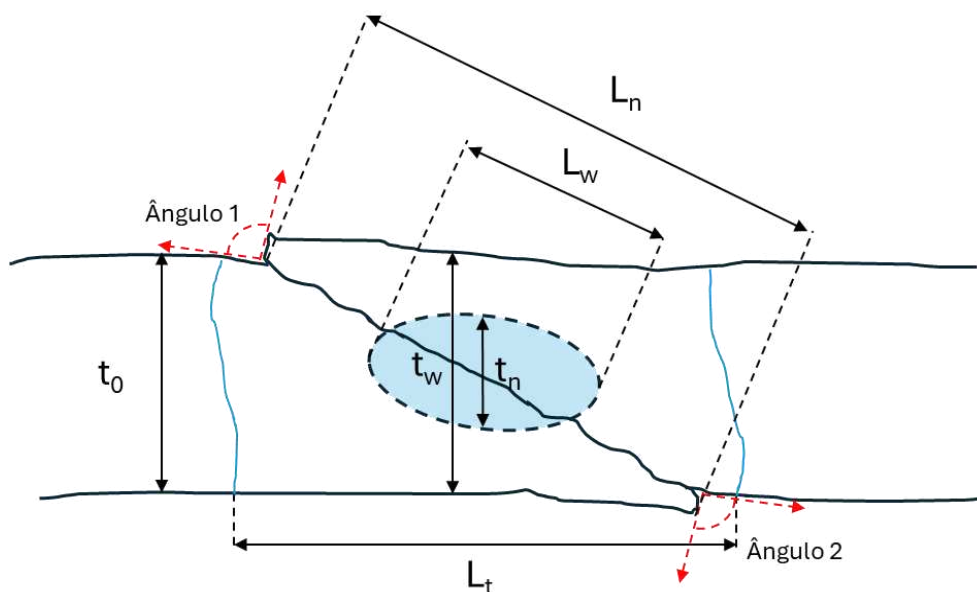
Parâmetro de avaliação geométrica da seção transversal da junta soldada.
